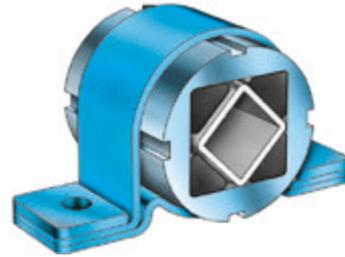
Aussengehäuse mit Befestigungsbride BK
